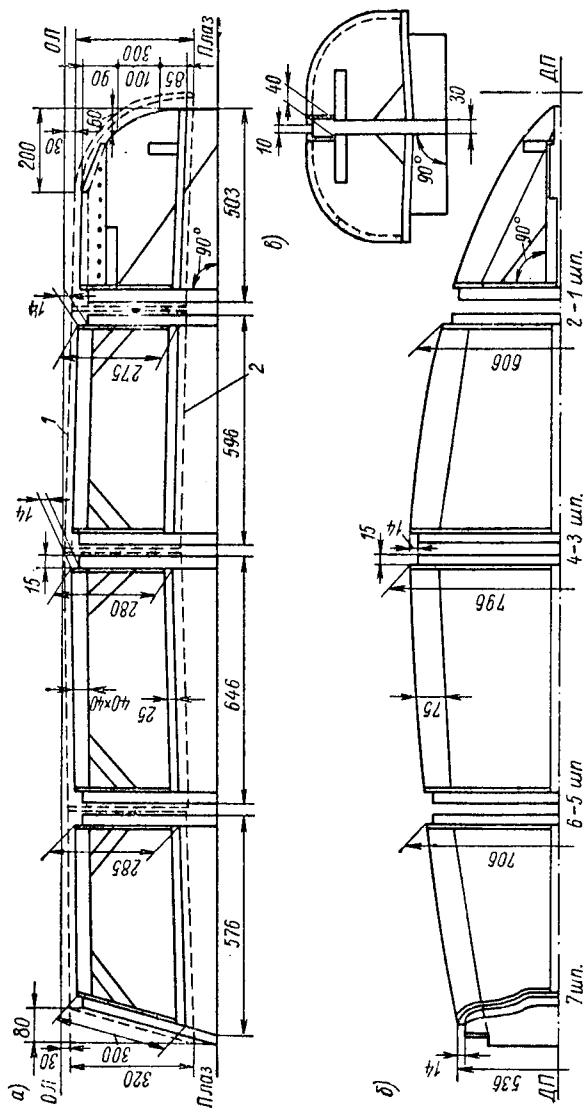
Кондуктор для лодки «Ладога» М1-А: а — вид сбоку, верх килем; б — план; в — вид спереди.
